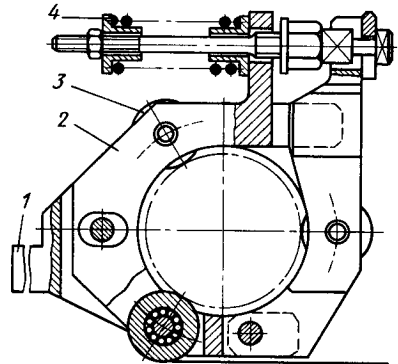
Трехроликовое приспособление для обкатывания нежестких валов: 1 — корпус; 2 — плавающая державка; 3 — ролик; 4 — пружина
